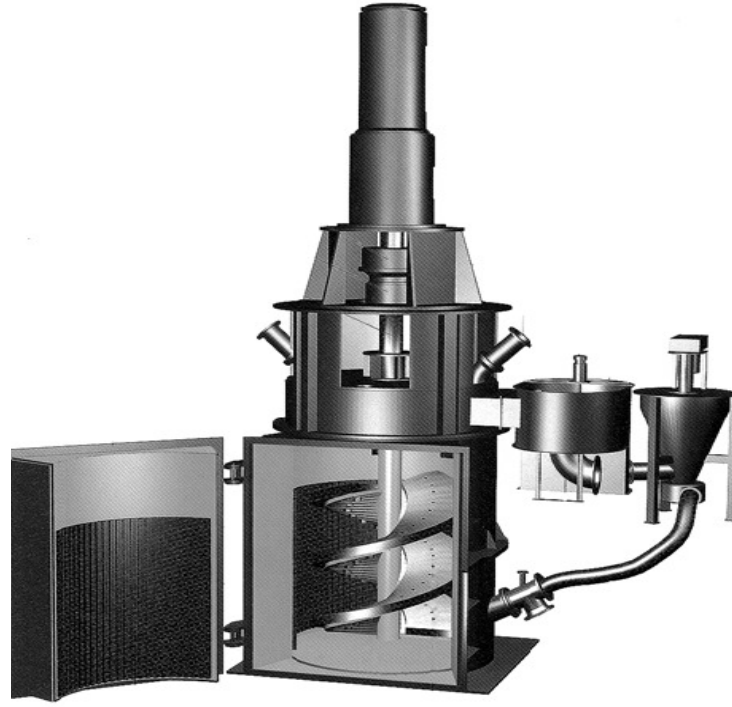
MaxxMill değirmeni genel tasarımı
